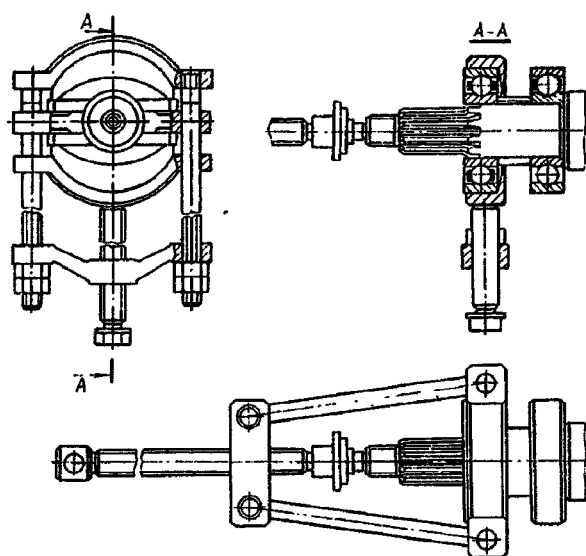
Снятие подшипников вала привода коробки отбора мощности
